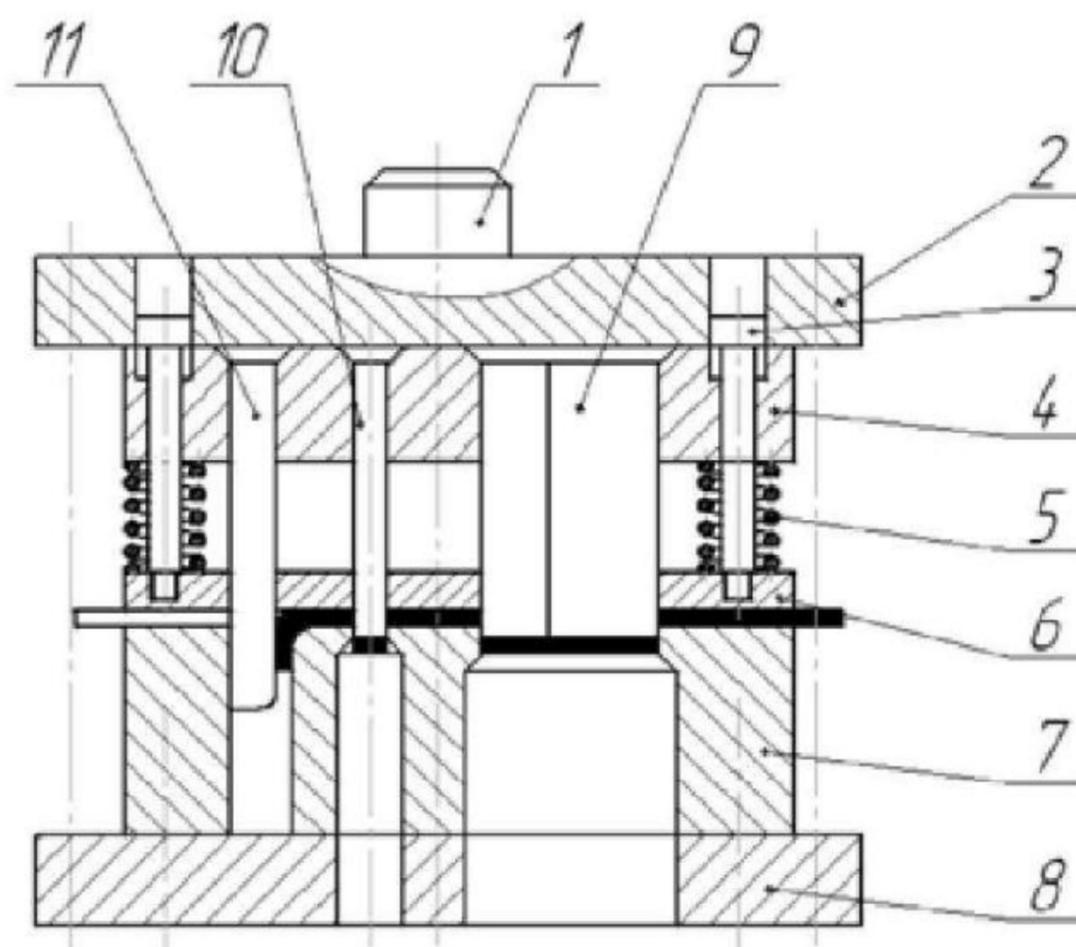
Схема штампа последовательного действия для пробивки, отрезки и гибки
